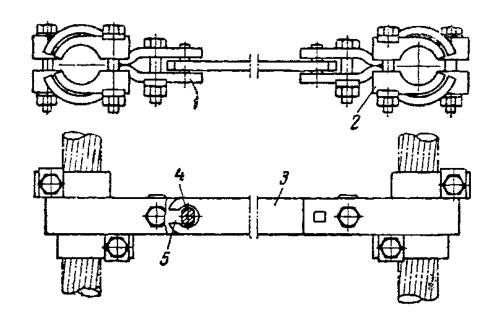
Распорка шарнирная: 1 — плашка; 2 — зажим, выполняется из алюминия; 3 — тяга; 4 — штифт; 5 — прорезь на тяге, выпускающей распорки
